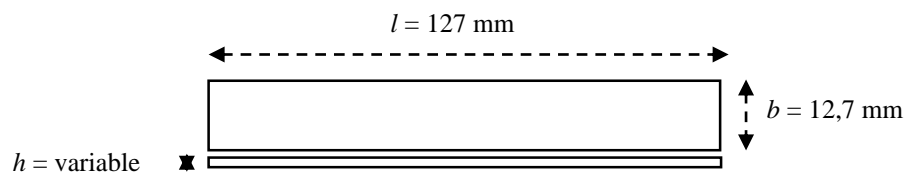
Dimensiones de probeta para ensayo de Impacto Charpy
